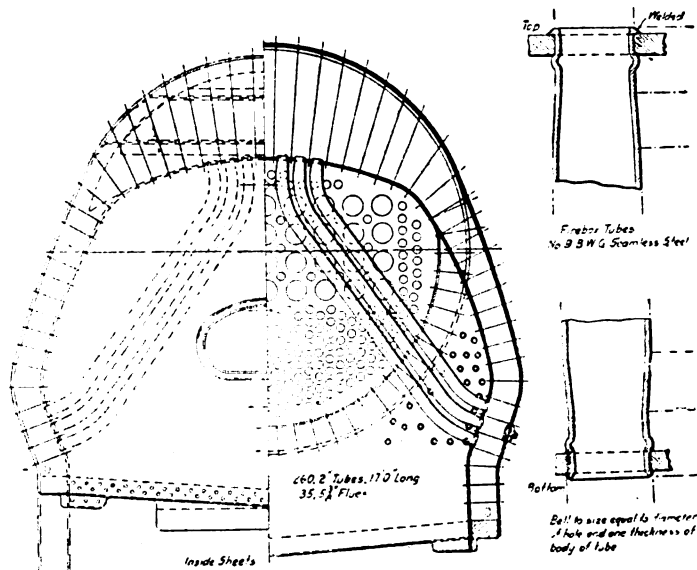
Sezione dal focolaio della caldaia a tubi d'acqua Riegel e disposizione schematica dei tubi d'acqua.
